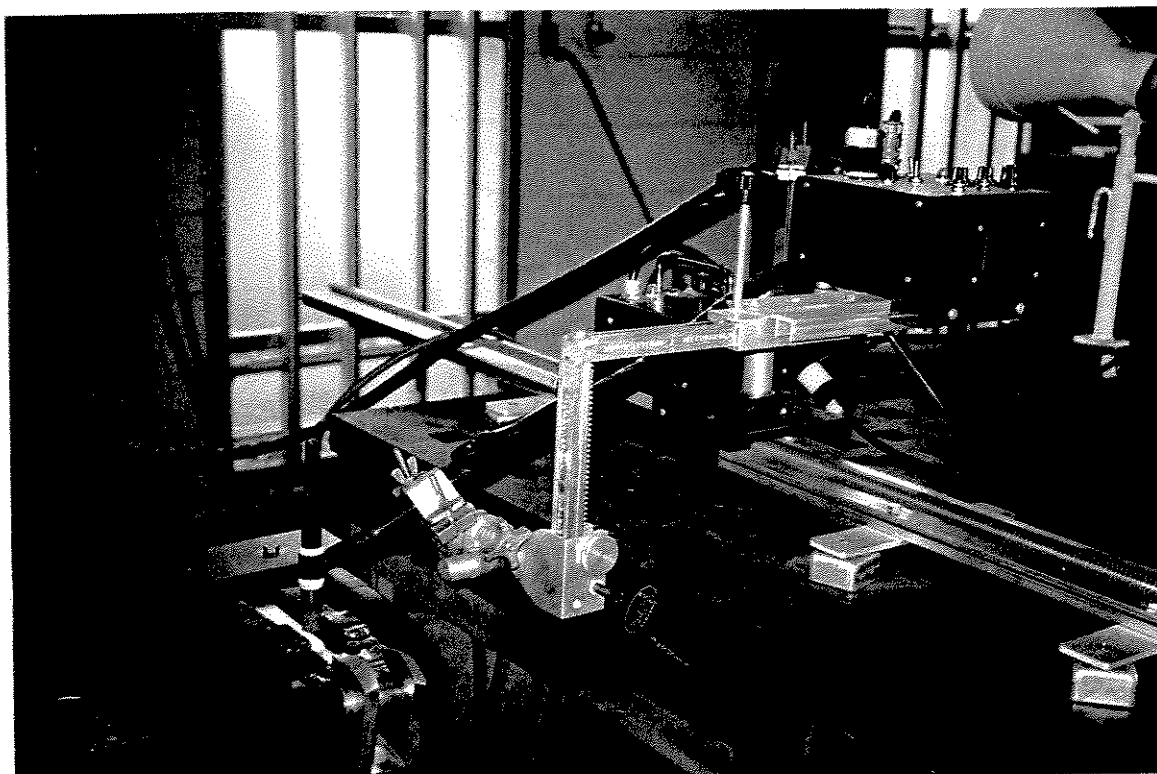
Dispositivo de movimentação da tocha de soldagem.
